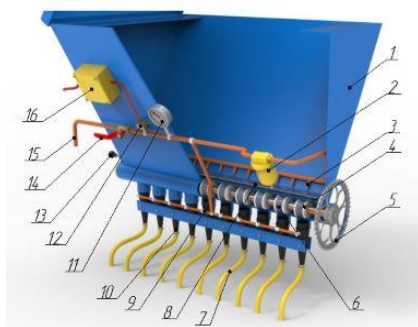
Схема высевающего аппарата пневматической сеялки: 1 – герметичный загрузочный бункер; 2 – воздушный фильтр осушитель; 3 – воздуховод высокого давления с соплами; 4 – прижимные кольца (фторопластовые); 5 – звездочка для связи с приводным колесом сеялки вала дозатора; 6 – дозирующие катушки; 7 – высевные патрубки; 8 – дозирующая планка; 9 – разряжающий воздуховод низкого давления с соплами; 10 – конусообразный направляющий высевной патрубков; 11 – манометр; 12 – электромагнитный клапан; 13 – регулировочная рукоятка дозирующей планки; 14 – регулировочный дроссель; 15 – воздушная магистраль; 16 – блок управления
